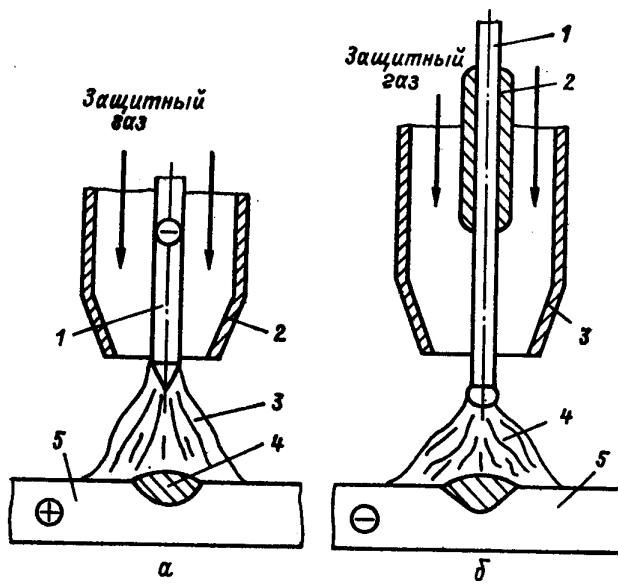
Схема процесса сварки в среде защитных газов:
